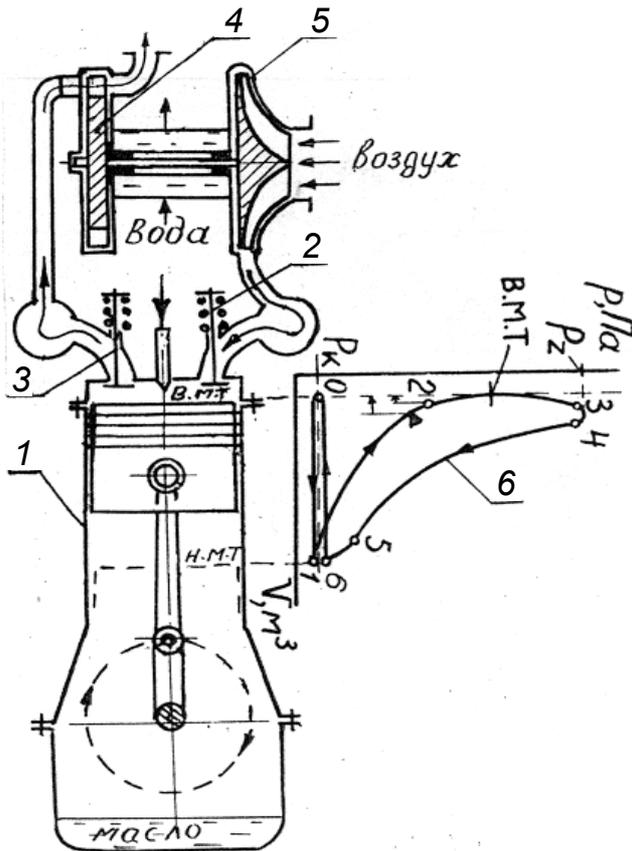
Четырехтактный дизель с наддувом: 1 – блок цилиндра; 2 – впускной клапан; 3 – выпускной клапан; 4 – газовая турбина; 5 – центробежный компрессор
